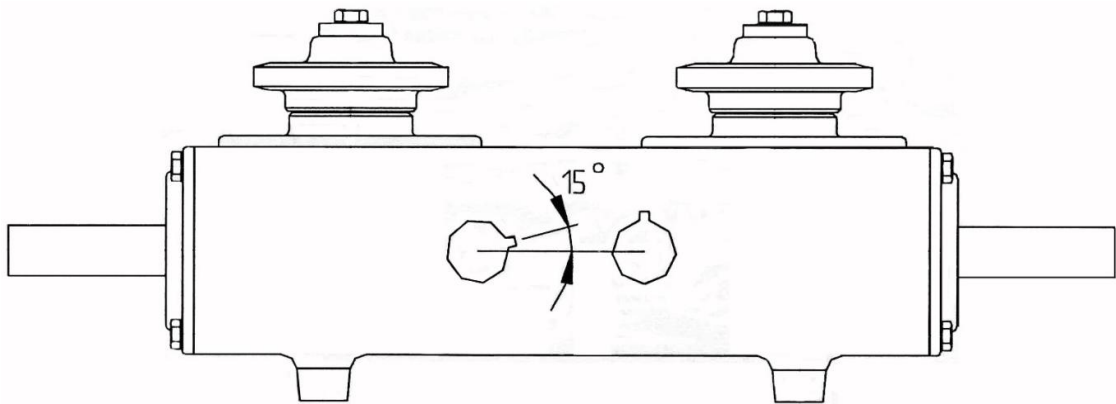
Установка положения шпонок на валах привода валцов жатки
